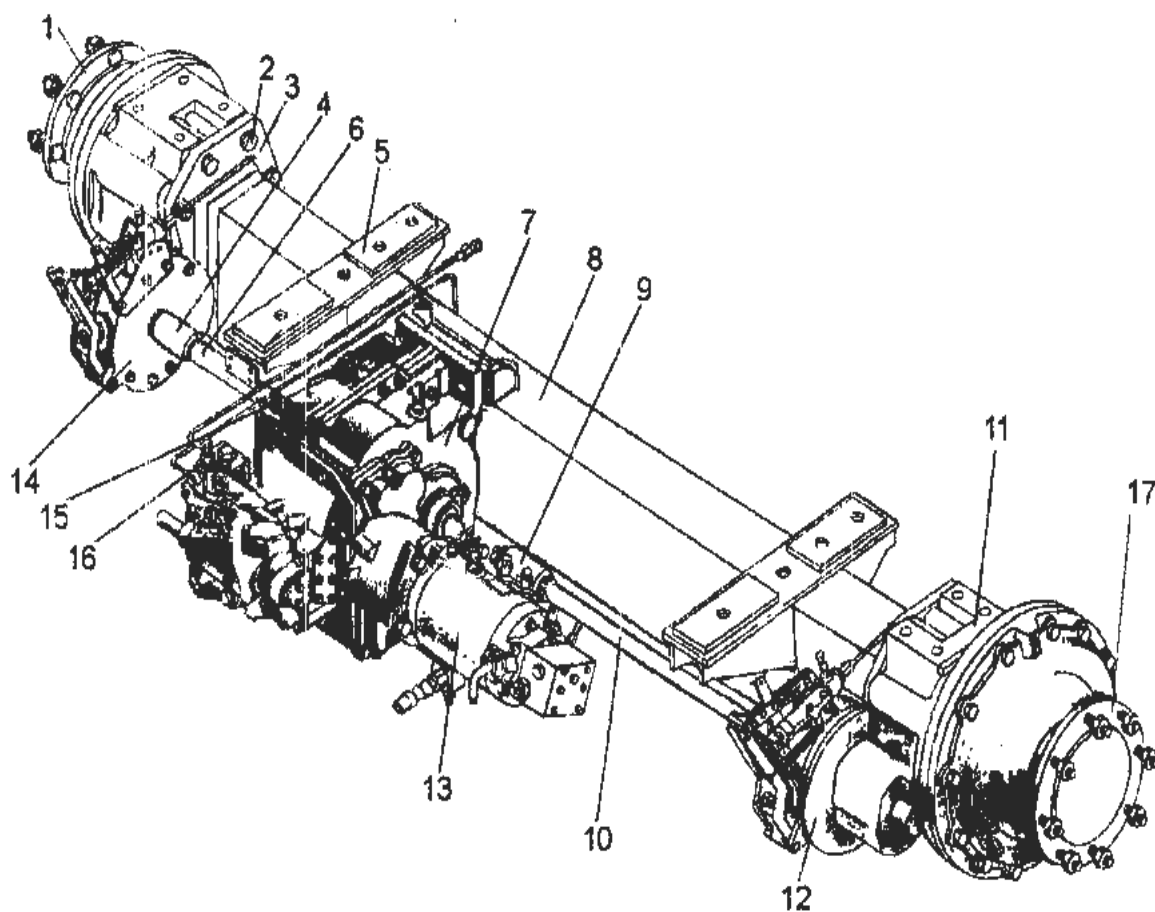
Мост ведущих колес МВГ-12: 1, 17 – фланцы; 2 – болты крепления редуктора; 3 – редуктор бортовой левой; 4 – втулка соединительная; 5 – кронштейн крепления моста; 6 – полуось левая; 7 – коробка диапазонов; 8 – балка моста; 9 – втулка соединительная; 10 – полуось правая; 11 – редуктор бортовой правой; 12 – дисковый тормоз правый; 13 – гидромотор; 14 – дисковый тормоз левый; 15 – датчик скорости; 16 – выключатель блокировки запуска
